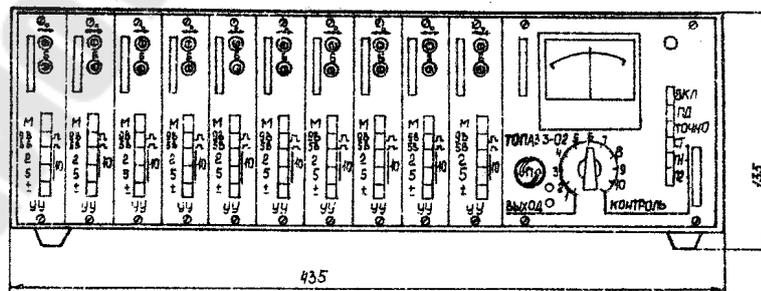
Внешний вид прибора ТОПАЗ-3-02
